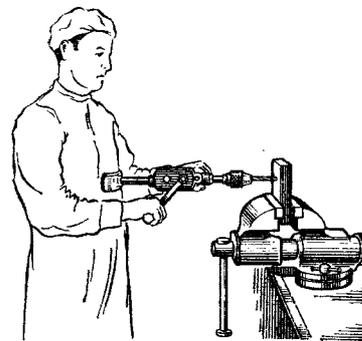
Сверление ручной дрелью горизонтальных отверстий
